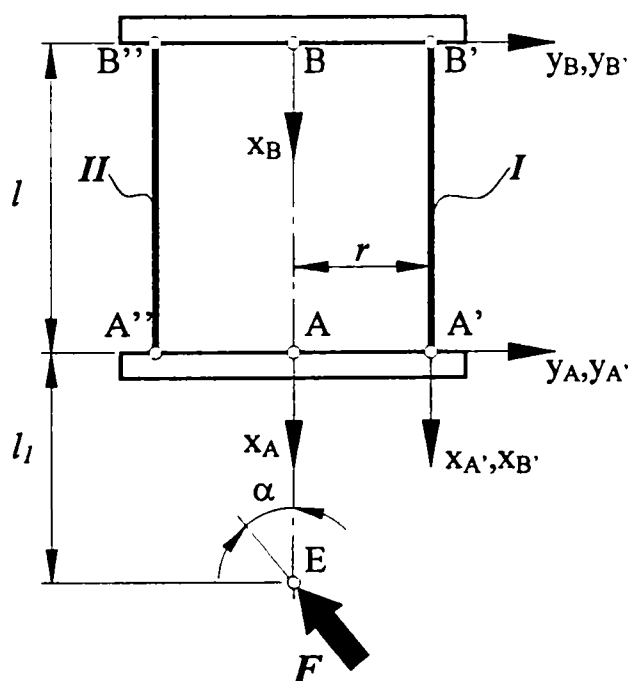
Schematizarea unui dispozitiv de complianță plan, cu două elemente elastice paralele
